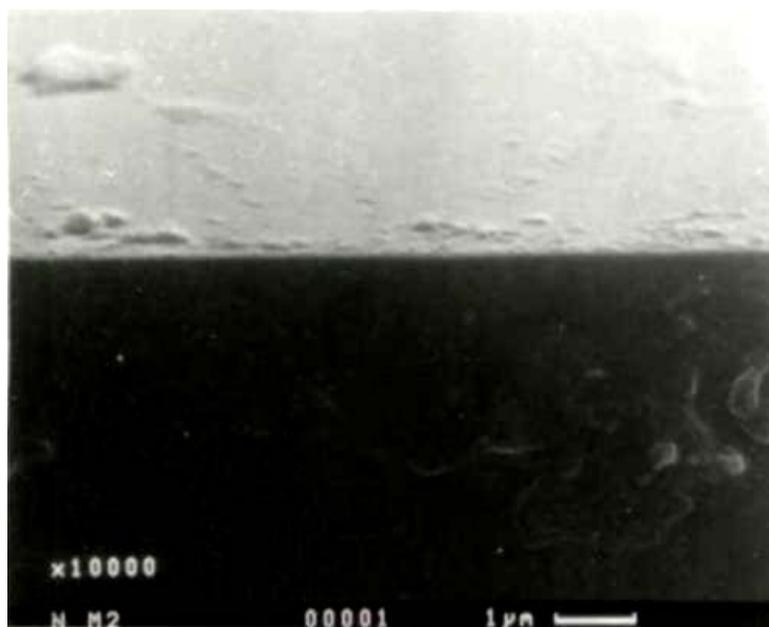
Режущая кромка нового алмазного резца, 10000^x;
